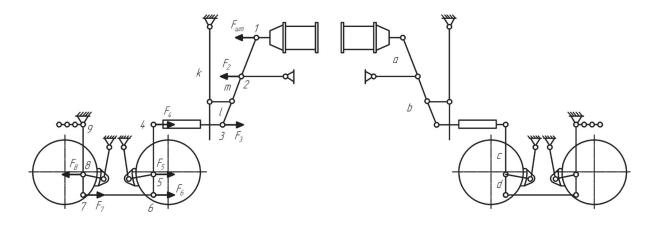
Схема типовой тормозной рычажной передачи грузового четырехосного вагона с потележечным торможением: 1...9 – точки соединения рычагов тормозной рычажной передачи
